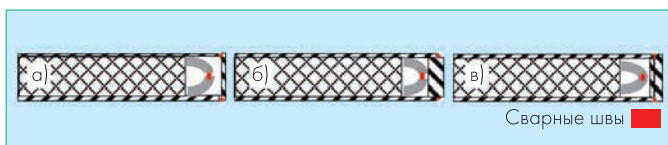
Типы сварных соединений термоэлектродных жил кабелей: а) кабель с плоским доньшком – соединением встык; б) кабель с внутренним цилиндрическим доньшком – соединение в угол; в) кабель с доньшком в виде пробки –соединение встык
